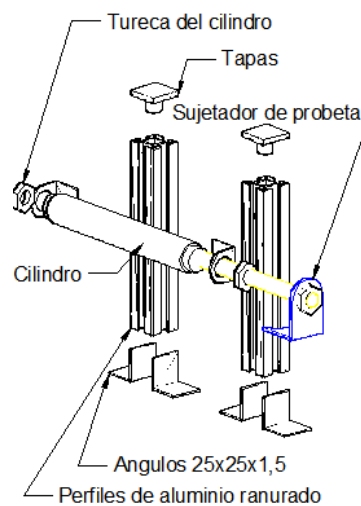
Dimensionamiento del soporte del cilindro expulsión
